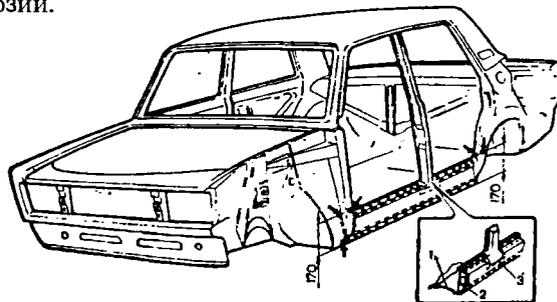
Замена порога двери: 1 - соединитель; 2 - усилитель порога; 3 - наружная панель порога. Пунктиром обозначены линии рубки, точками - швы контактной сварки. Стрелками показаны места газовой сварки
